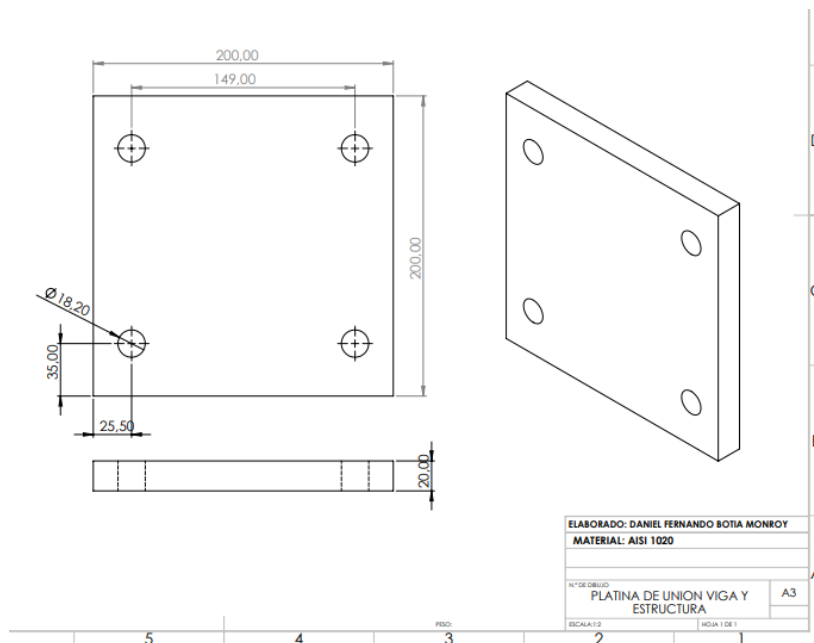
Diseño de la platina de unión viga – estructura. Fuente: Autor
